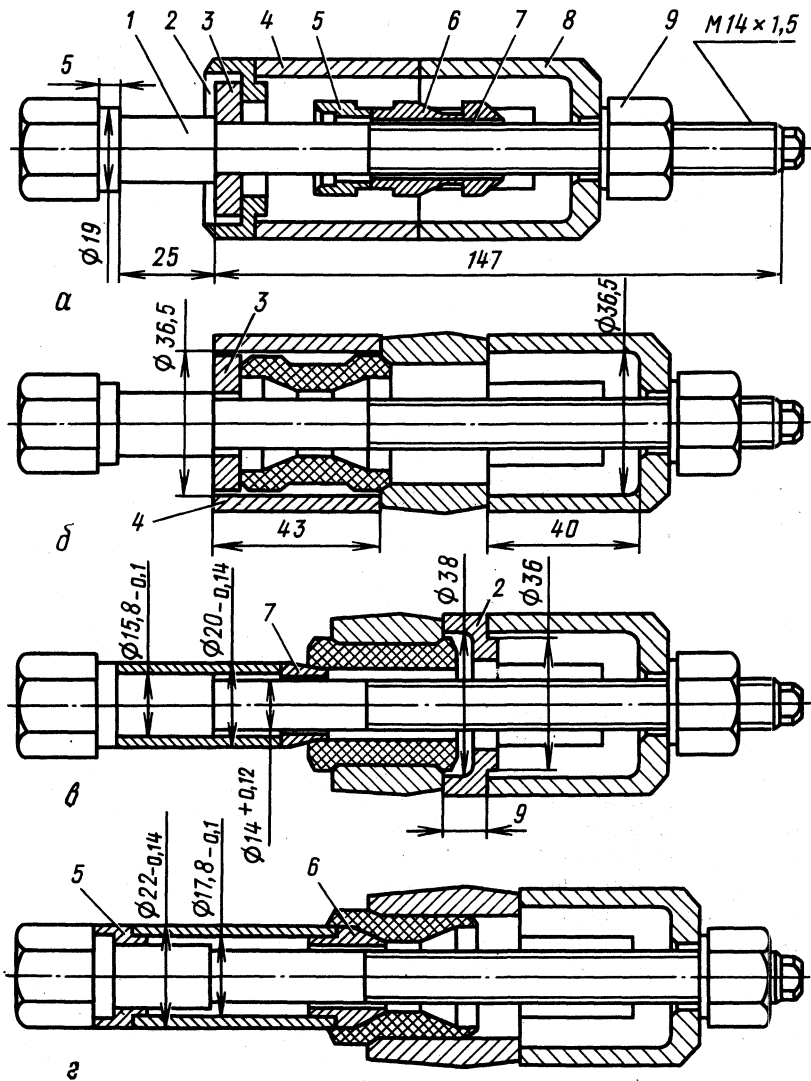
Приспособление для замены резиновых втулок рычагов передней подвески автомобиля ГАЗ-24 «Волга»:
